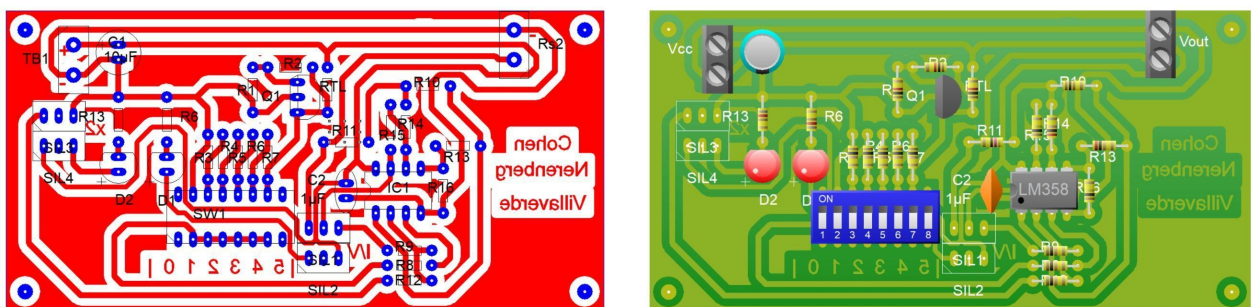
PCB del circuito realizado en PCB Wizard [7]
